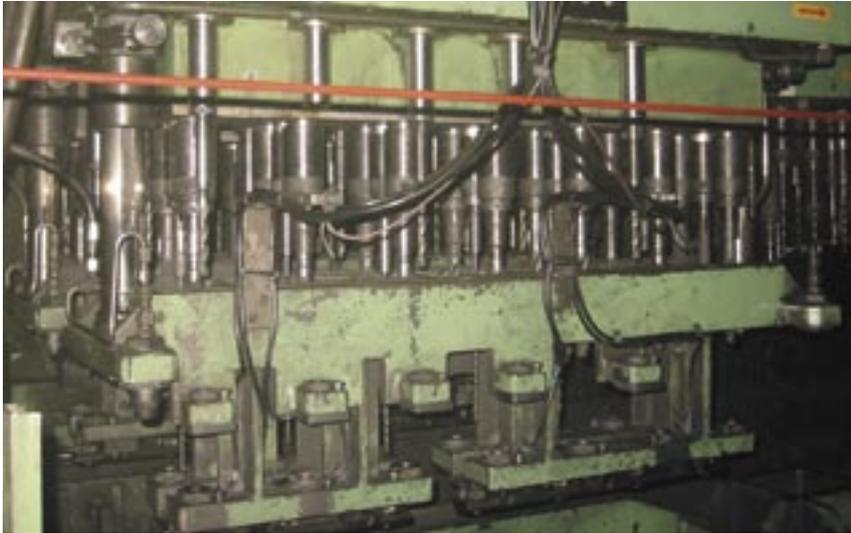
Komplexer Mehrspindelbohrkopf: Eine Herausforderung für die Werkzeugüberwachung
